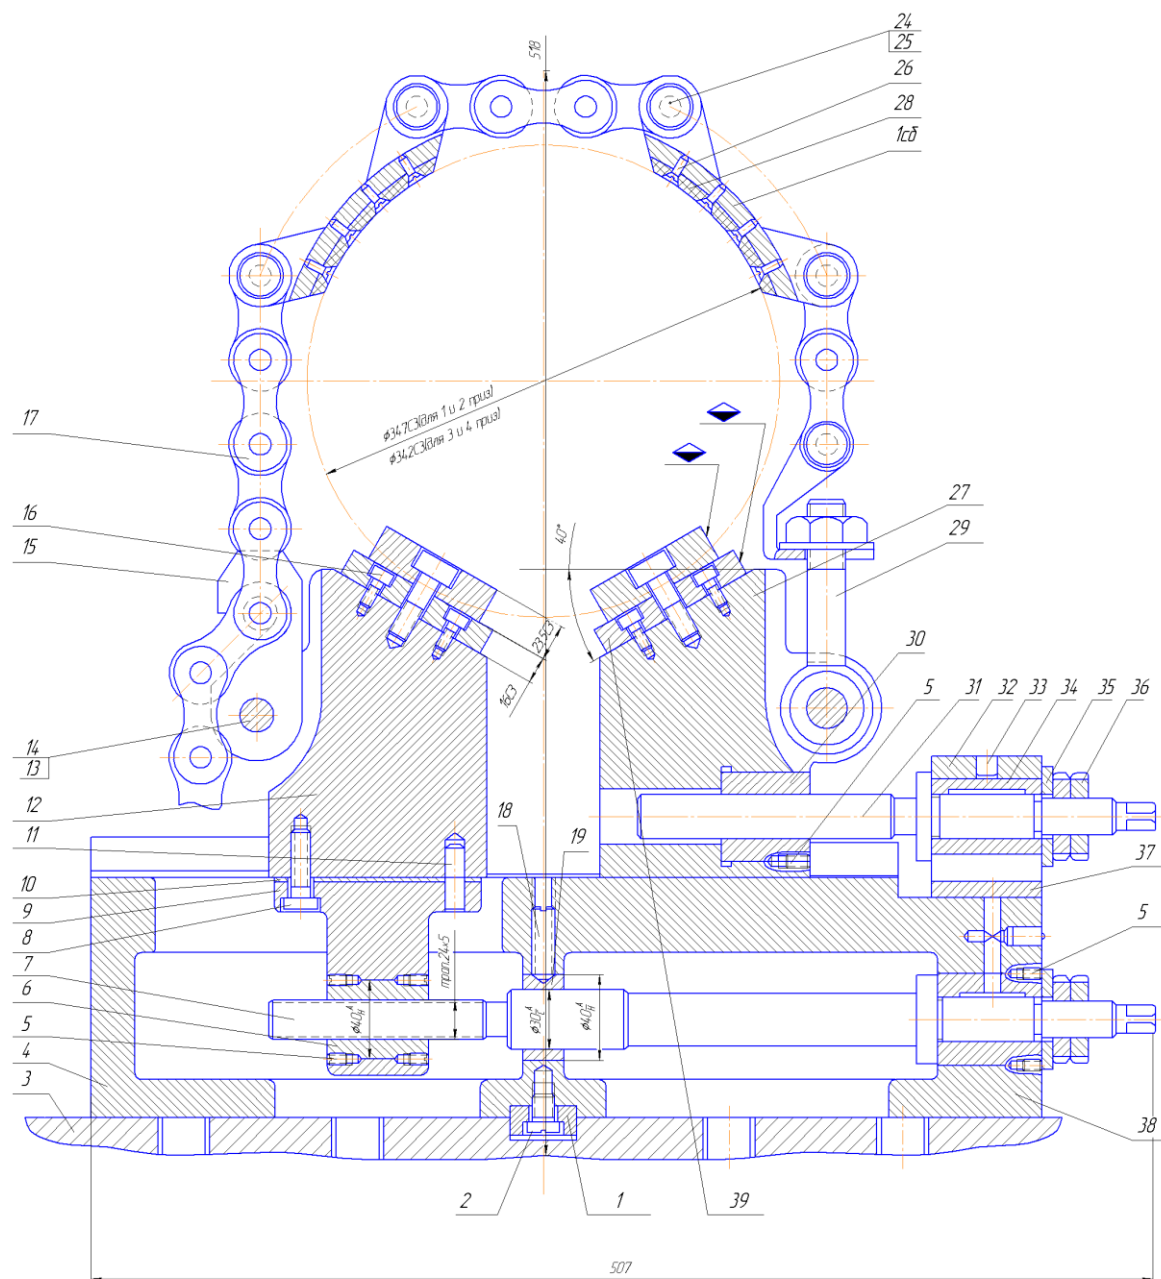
Пристосування для розточки втулок робочого циліндру великих розмірів
